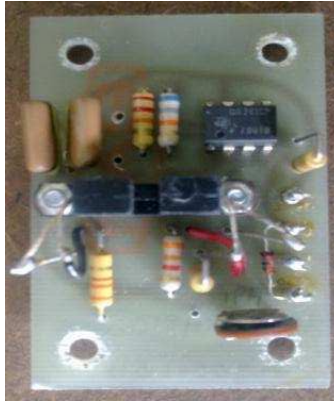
20 Estado Inicial de la Máquina de Ensayos Universales - Circuito Encoder
